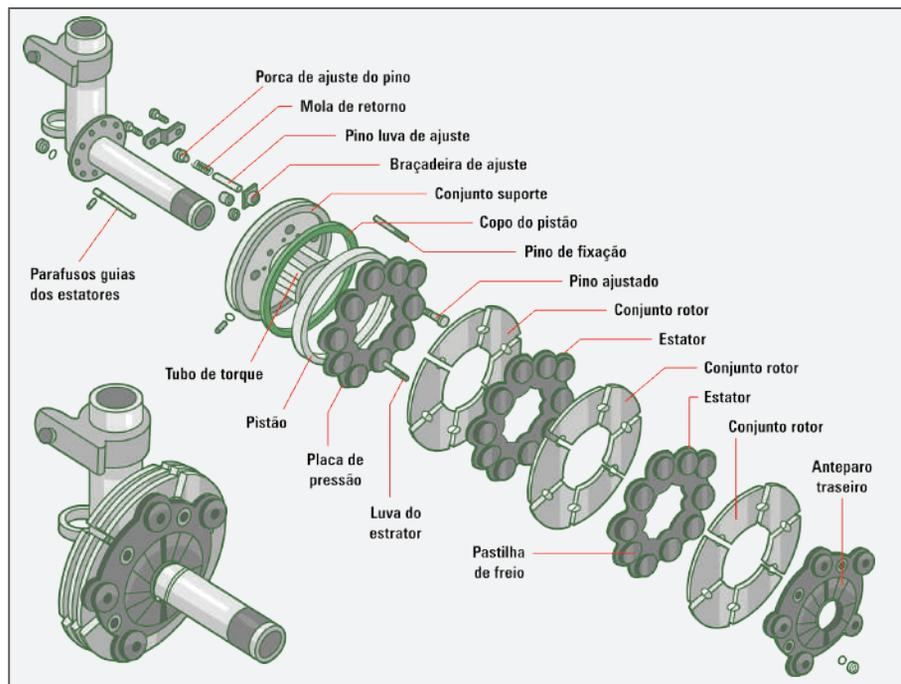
Unidades de um conjunto de freio de rotor segmentado
